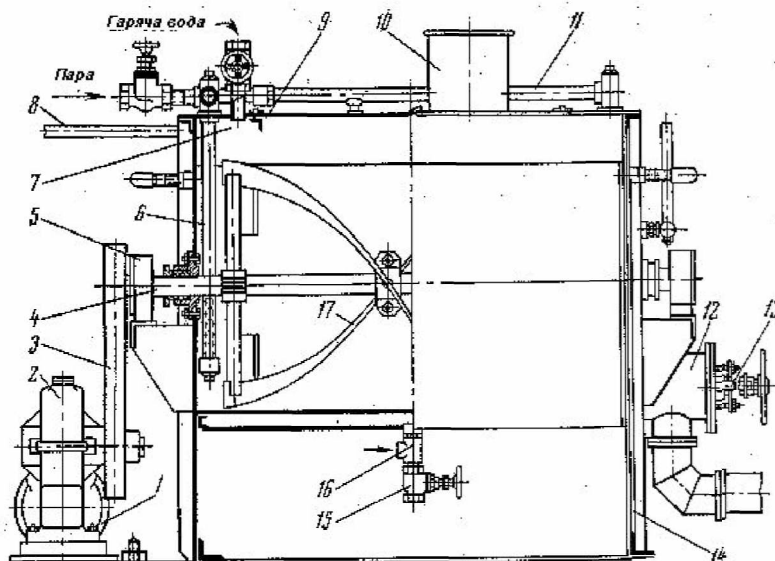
Заварювальна машина ХЗМ-300: 1 – електродвигун; 2 – редуктор; 3 – ланцюгова передача; 4 – горизонтальний вал; 5 – підшипники; 6 – барботер пари; 7 – ємкість; 8 – труба виходу води; 9 – відкидна кришка; 10 - патрубок борошна і солоду; 11 – труба подавання гарячої води; 12 – патрубок готової заварки; 13 – затвор; 14 – стійки.
